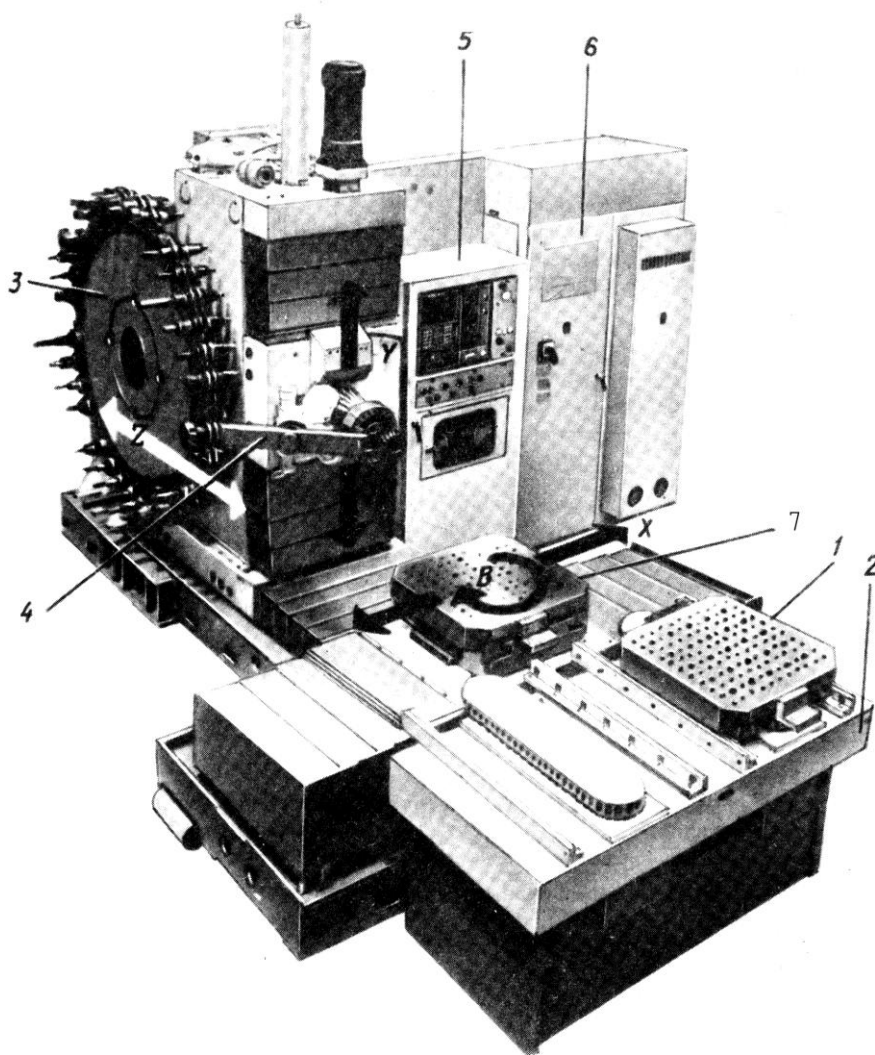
Компоновка ГПМ для обработки корпусных деталей:
